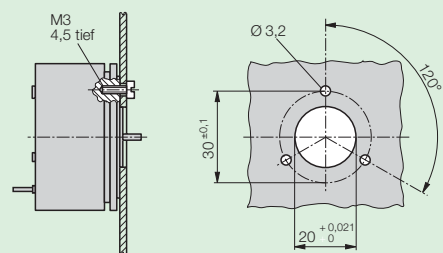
Bohrplan für Befestigung mit 3 Zylinderschrauben M3.
